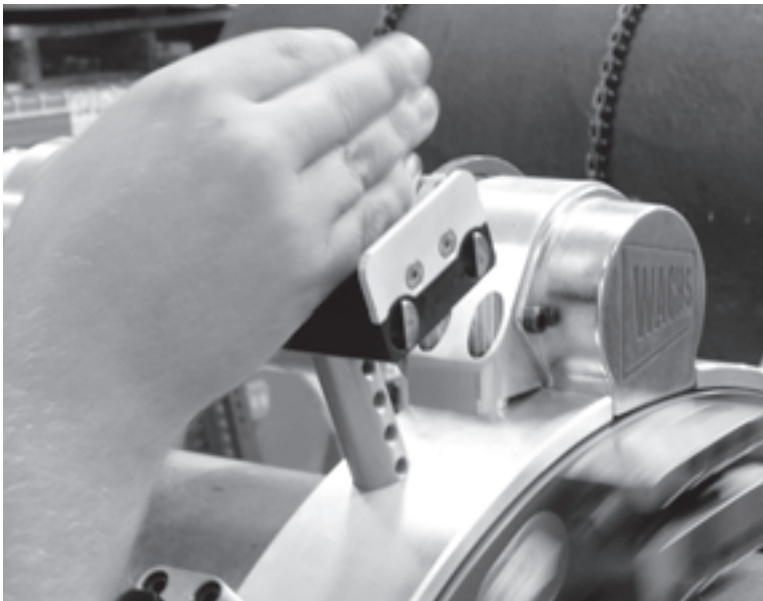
Poussez de nouveau la goupille du déclencheur pour désengager le déclencheur, avant de démarrer la machine.
